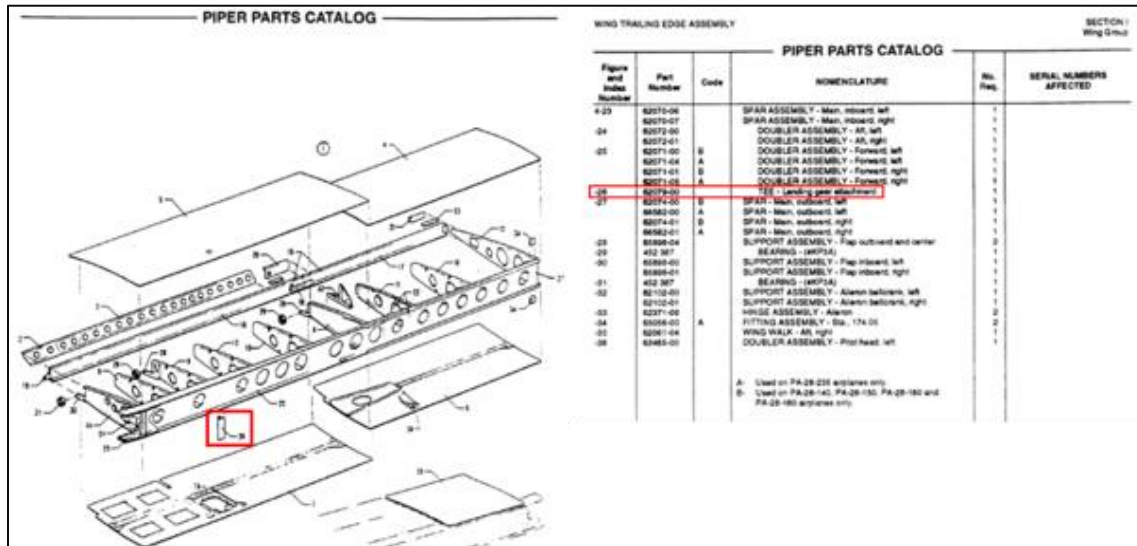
Soporte estructural (tee) del tren de aterrizaje con el plano de la aeronave.
